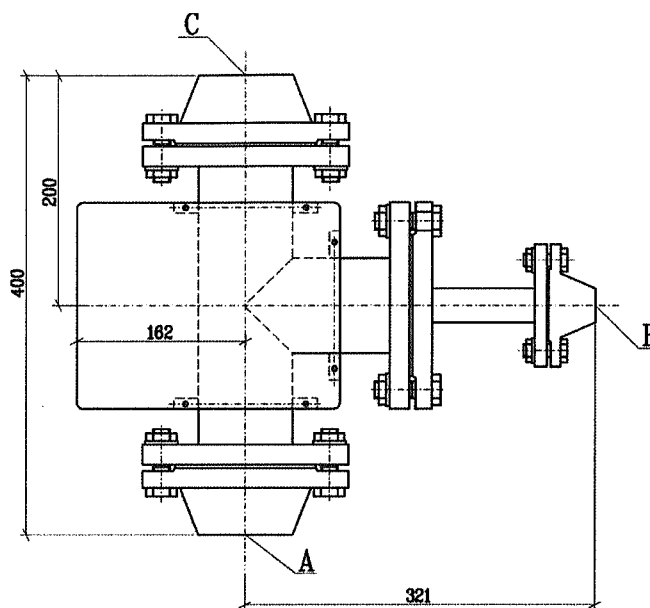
Габаритный чертеж смесителя приготовления регенерационных растворов кислоты LDB70AM001
